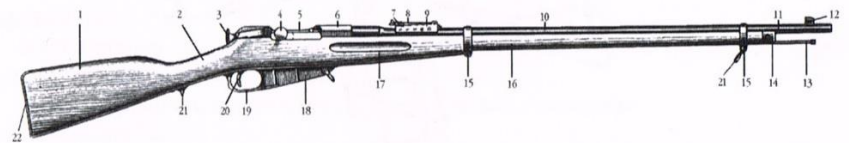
Элементы конструкции винтовки образца 1891/1930 г. конструкции С.И. Мосина:
